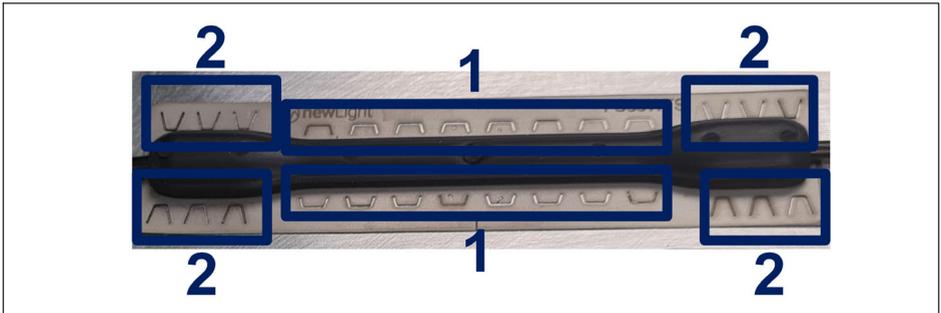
Schweißflächen des FS63CTS
